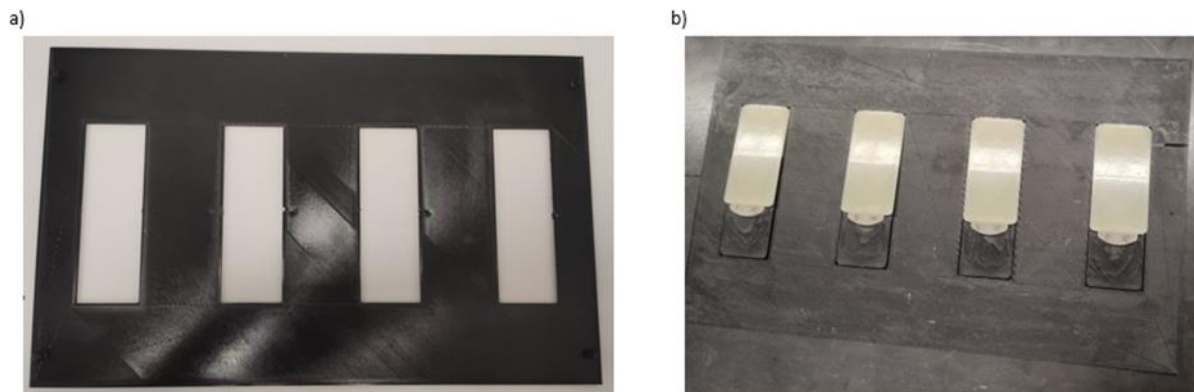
a) placa de PLA; b) peças posicionadas para a soldadura
